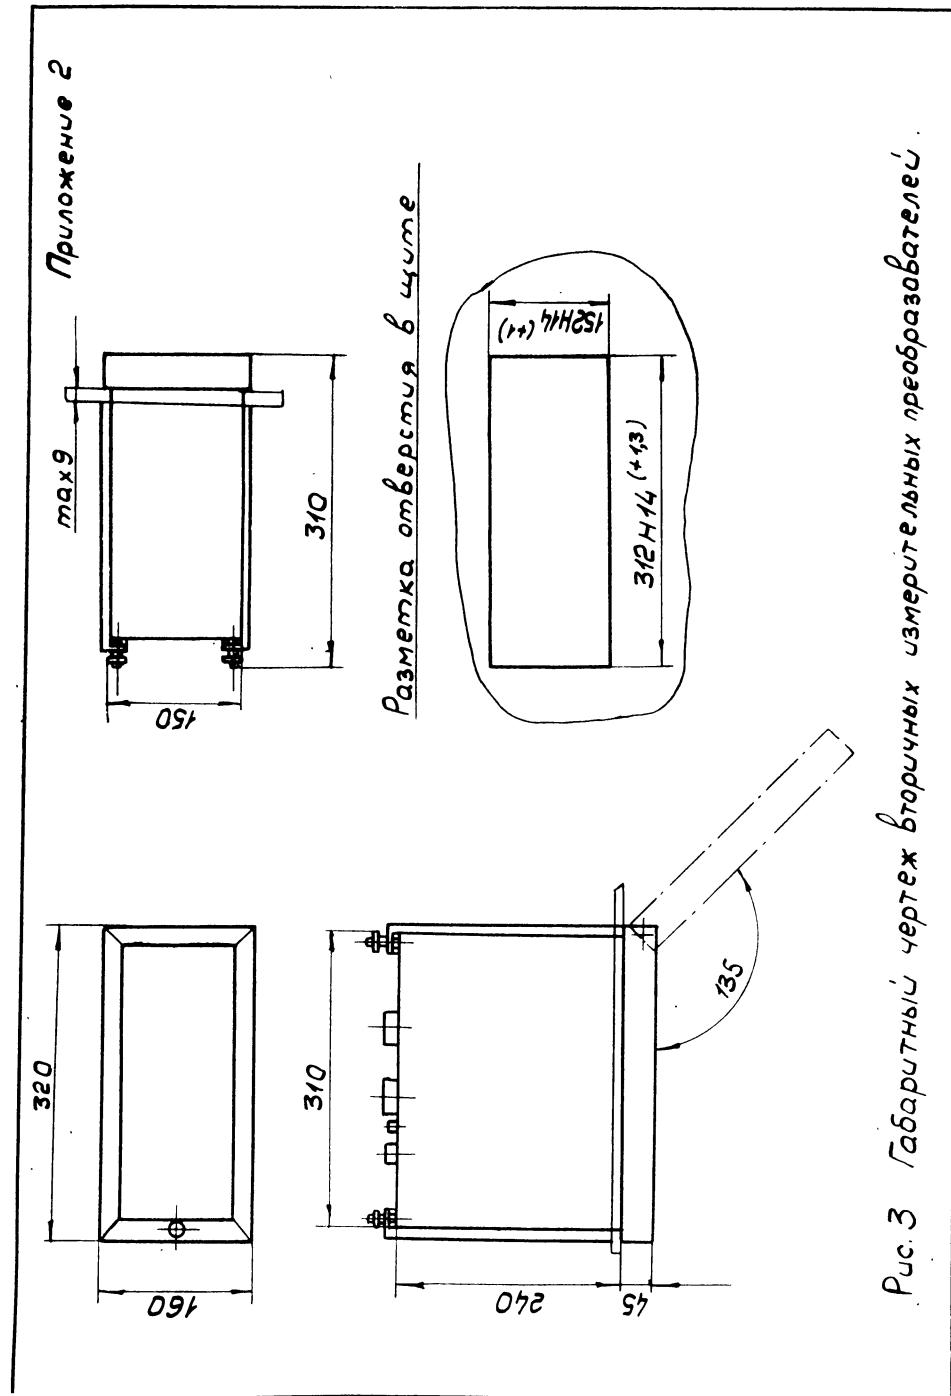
Габаритный чертеж вторичных измерительных преобразователей
